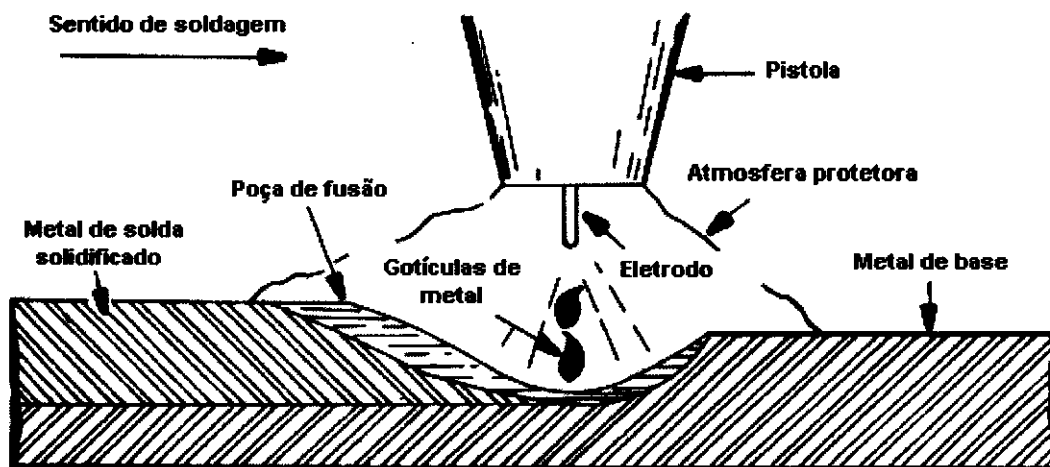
Soldagem MIG/MAG (FBTS, 1987).
